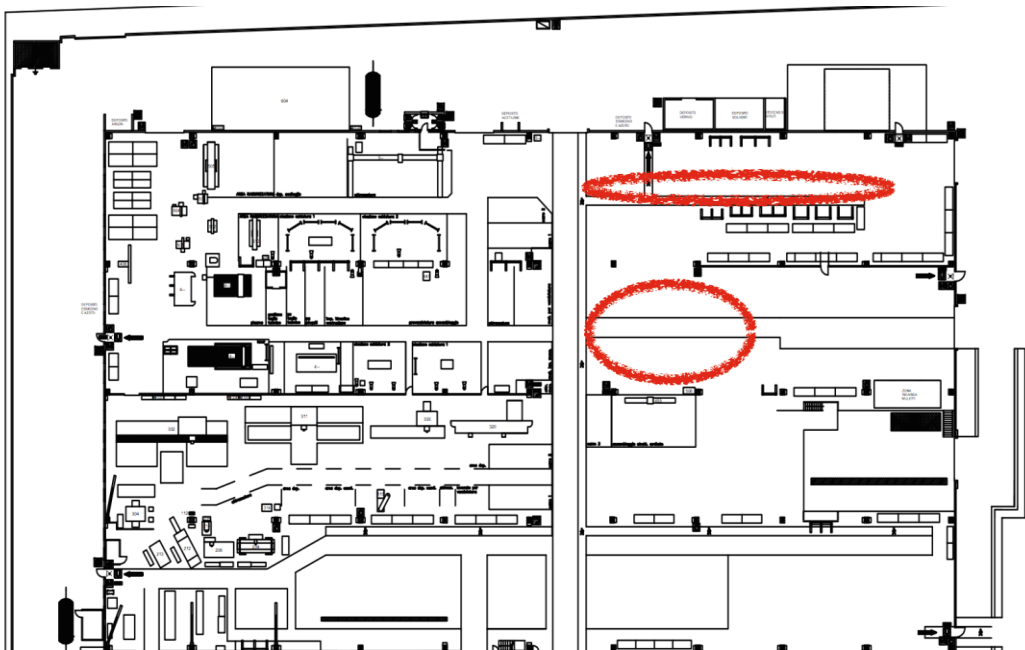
11: Localizzazione sulla pianta dello stabilimento delle due aree di raccolta componenti
